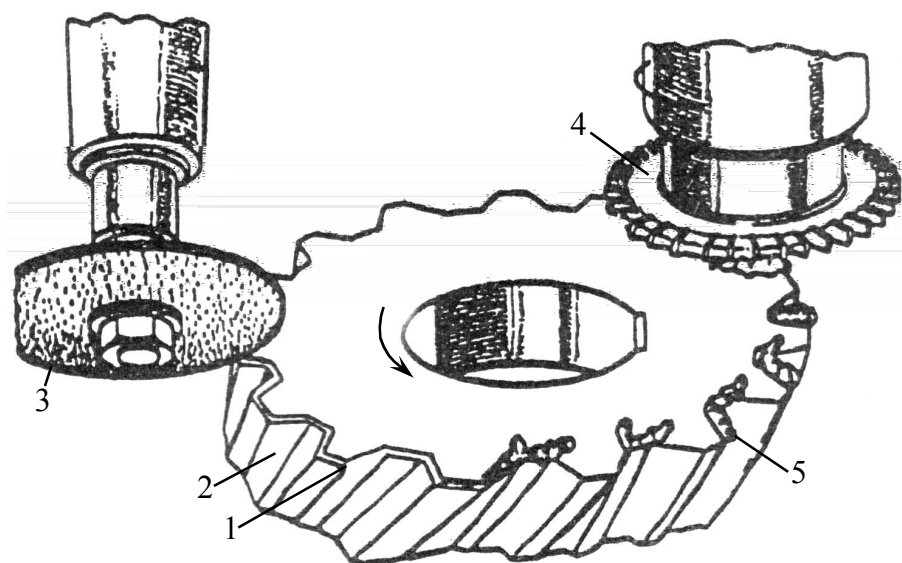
Схема снятия фасок цилиндрическим плавающим кругом и заусенец фрезой: 1 – снятая фаска; 2 – зубчатое колесо; 3 – дисковый круг; 4 – фреза; 5 – заусенец
